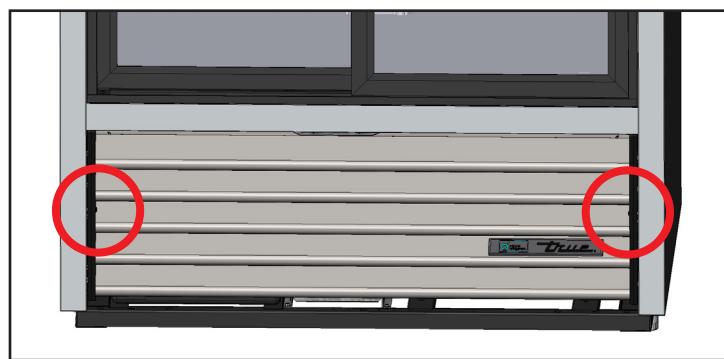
Винты крепления жалюзийной решетки под раздвижными дверцами
